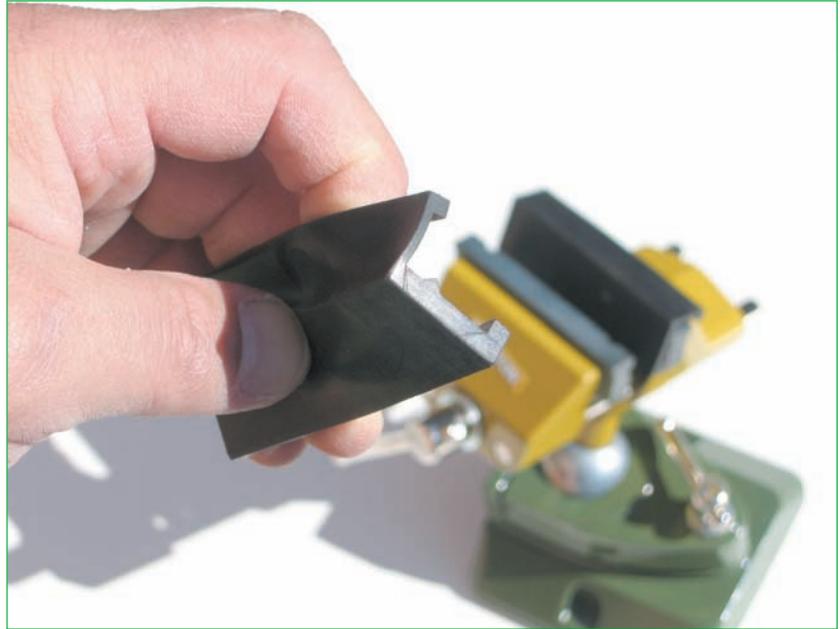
Feinmechaniker-Schraubstöcke eignen sich bestens für Lötáufgaben.
